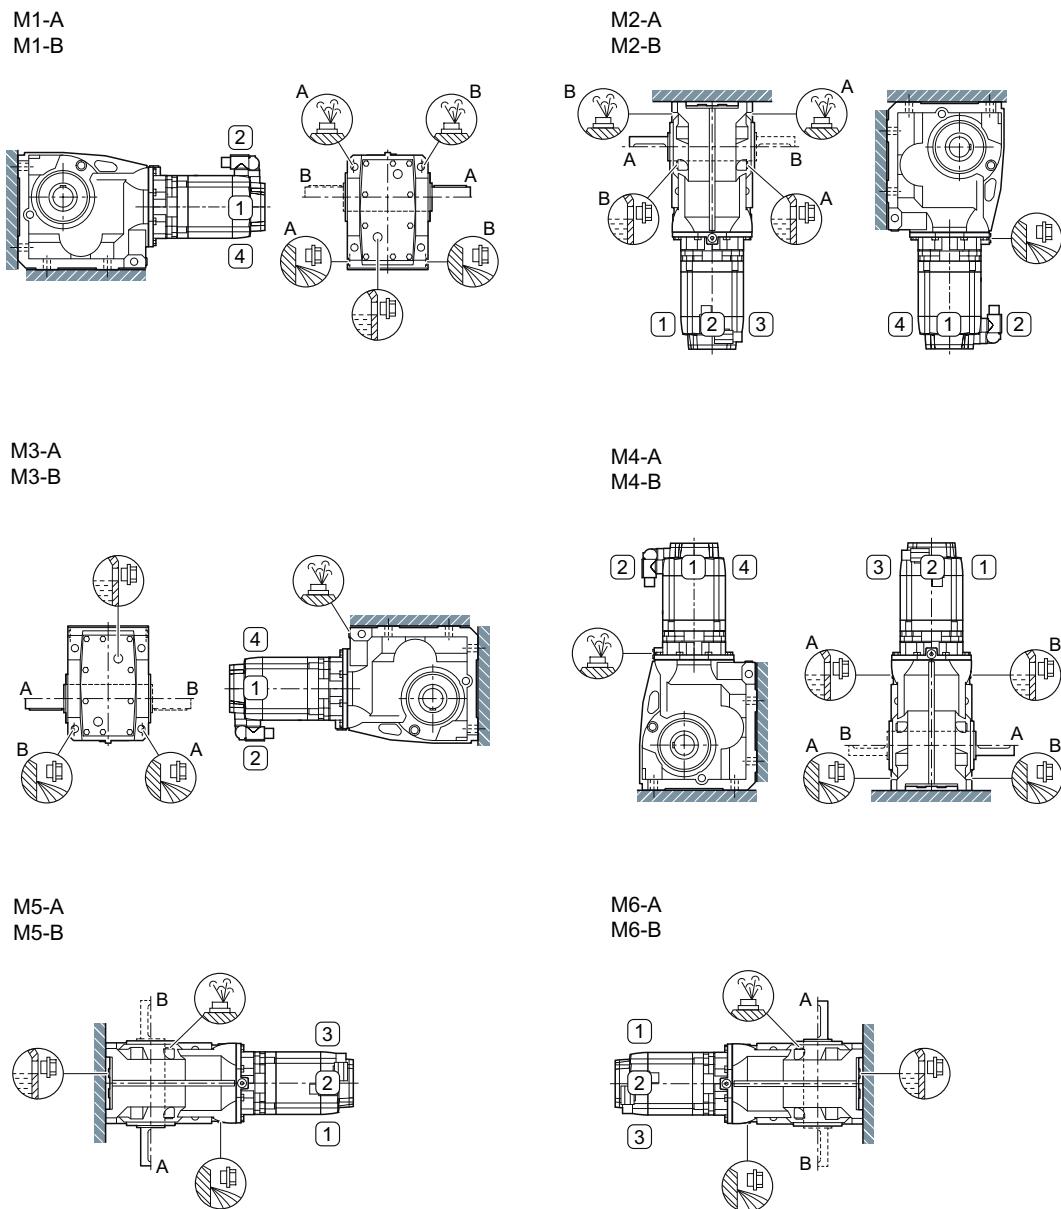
Einbaulagen für Servo-Kegelradgetriebemotor K, Fußausführung, Baugrößen 39 - 149, 3-stufig
